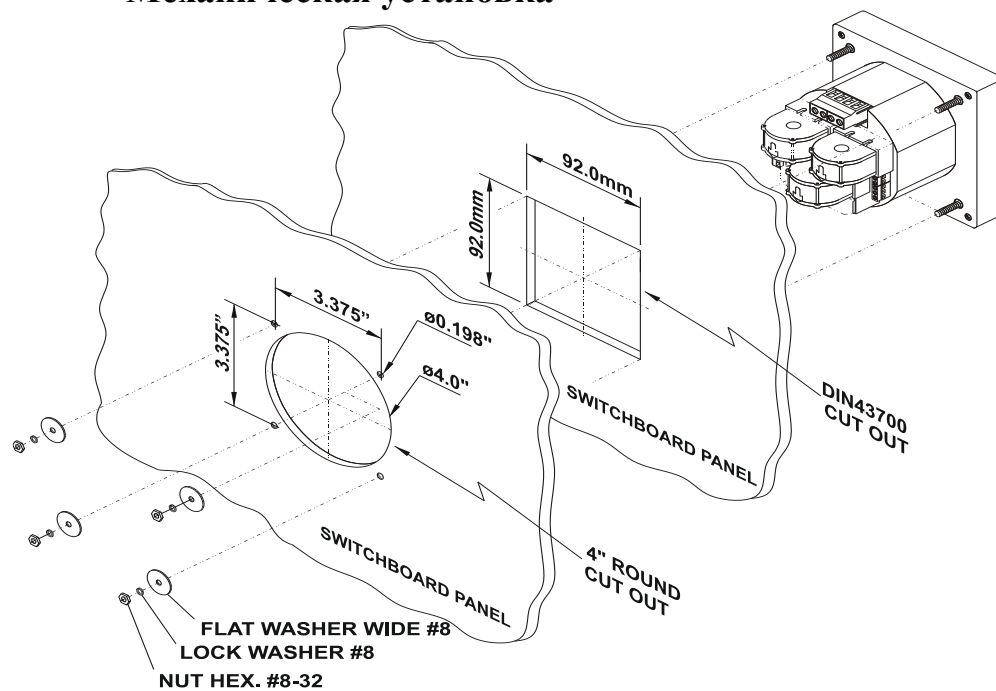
Монтаж РМ130/РМ135 PLUS (прямоугольный или круглый вырез)
